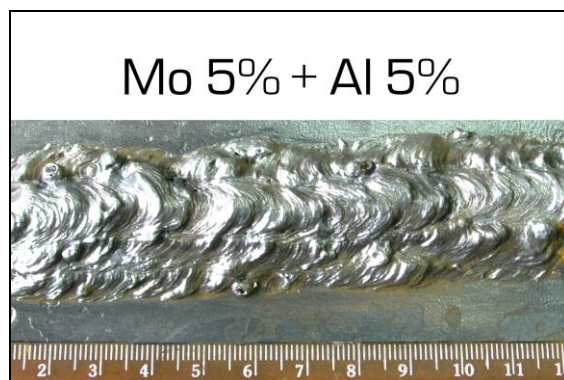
Зовнішній вигляд зварного шва при підводному зварюванні.
